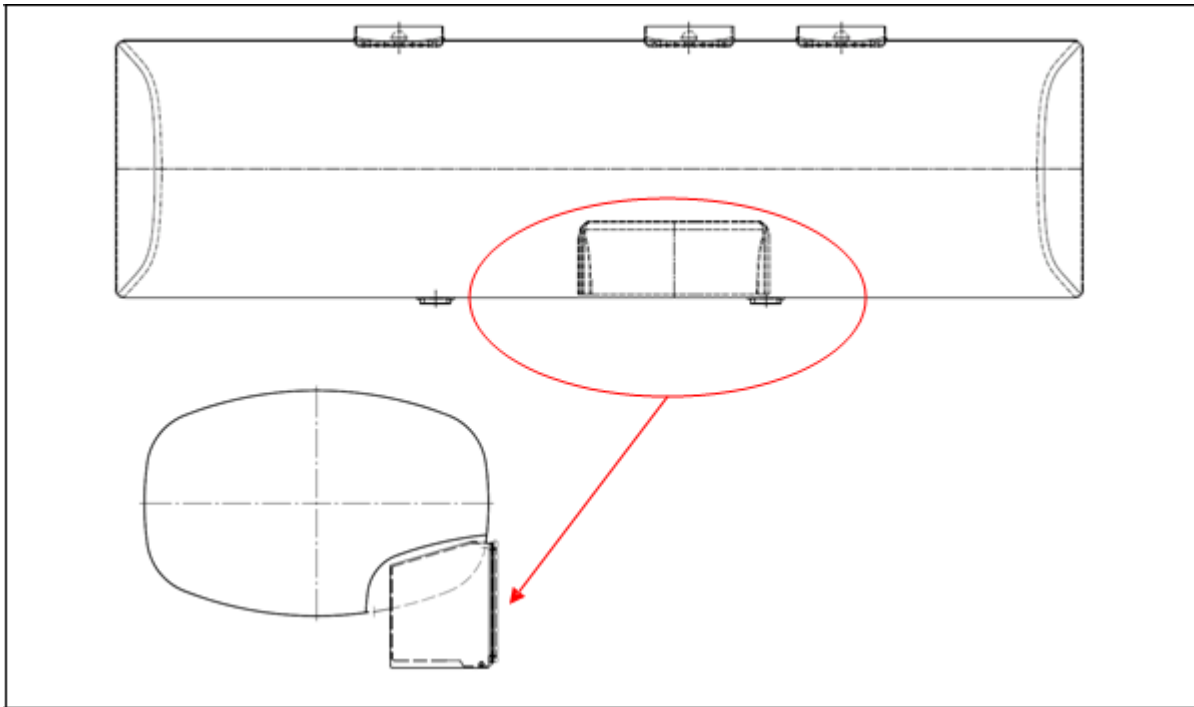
Kofferförmiger Tank, mit Ausschnitt für Armaturenschrank
